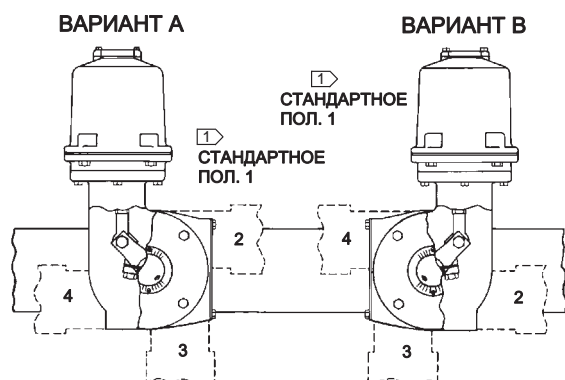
Варианты конструкции корпуса привода и монтажные положения
